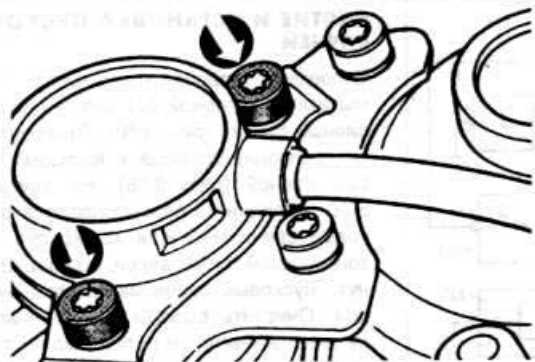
Стрелками показаны винты крепления корпуса датчика положения дроссельной заслонки
